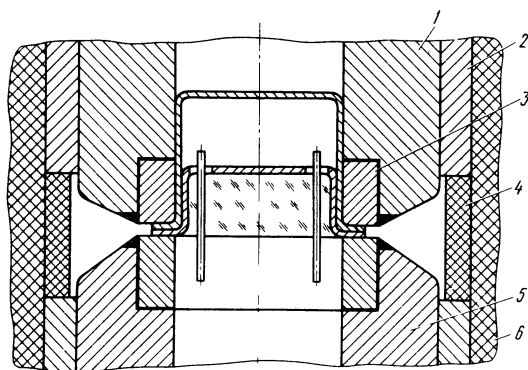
Сварочный инструмент для герметизации корпусов контактной контурной электросваркой: 1, 5 — державки электродов, 2, 4 — стальная и изолирующая втулки, 3 — вставки, 6 — текстолитовый стакан
